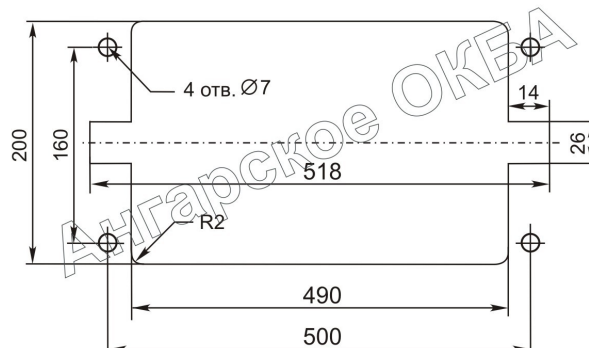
Габаритно-установочный чертеж газоанализатора
